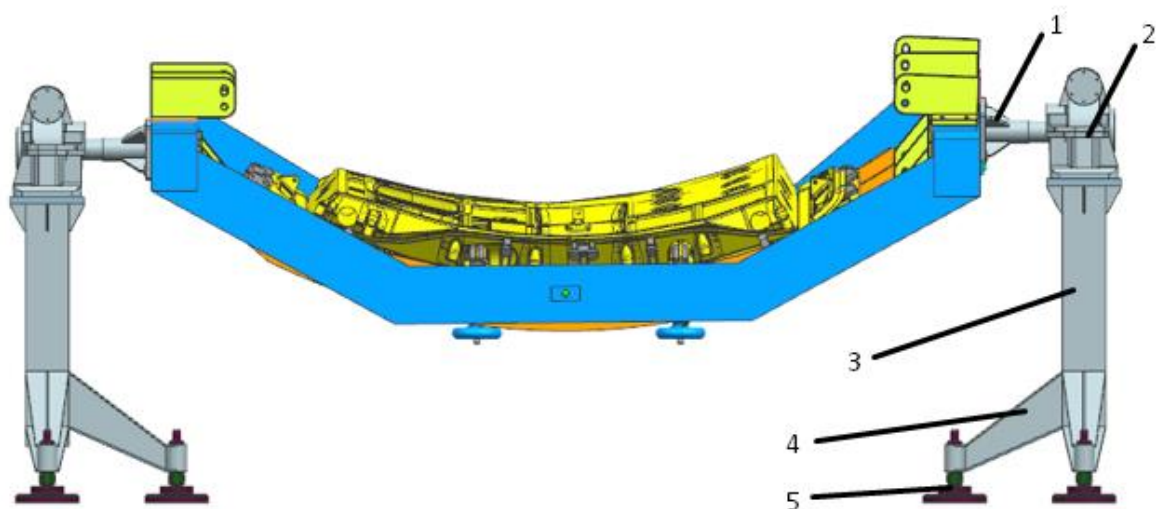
Поворотный механизм сборочного приспособления двери: 1- цапфы; 2- редуктор; 3 – стойка; 4 – ножки; 5 – лапки.
